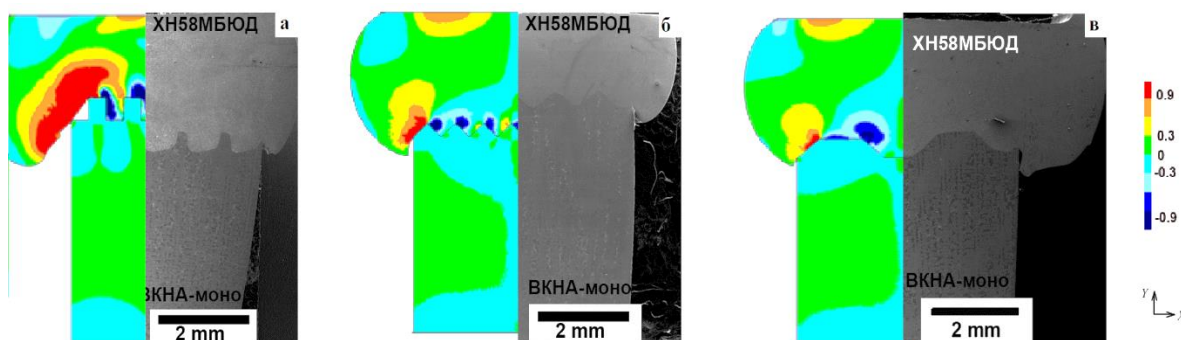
Физическое и компьютерное моделирование сварных образцов с различной формой рельефа на поверхности интерметаллидного сплава.
